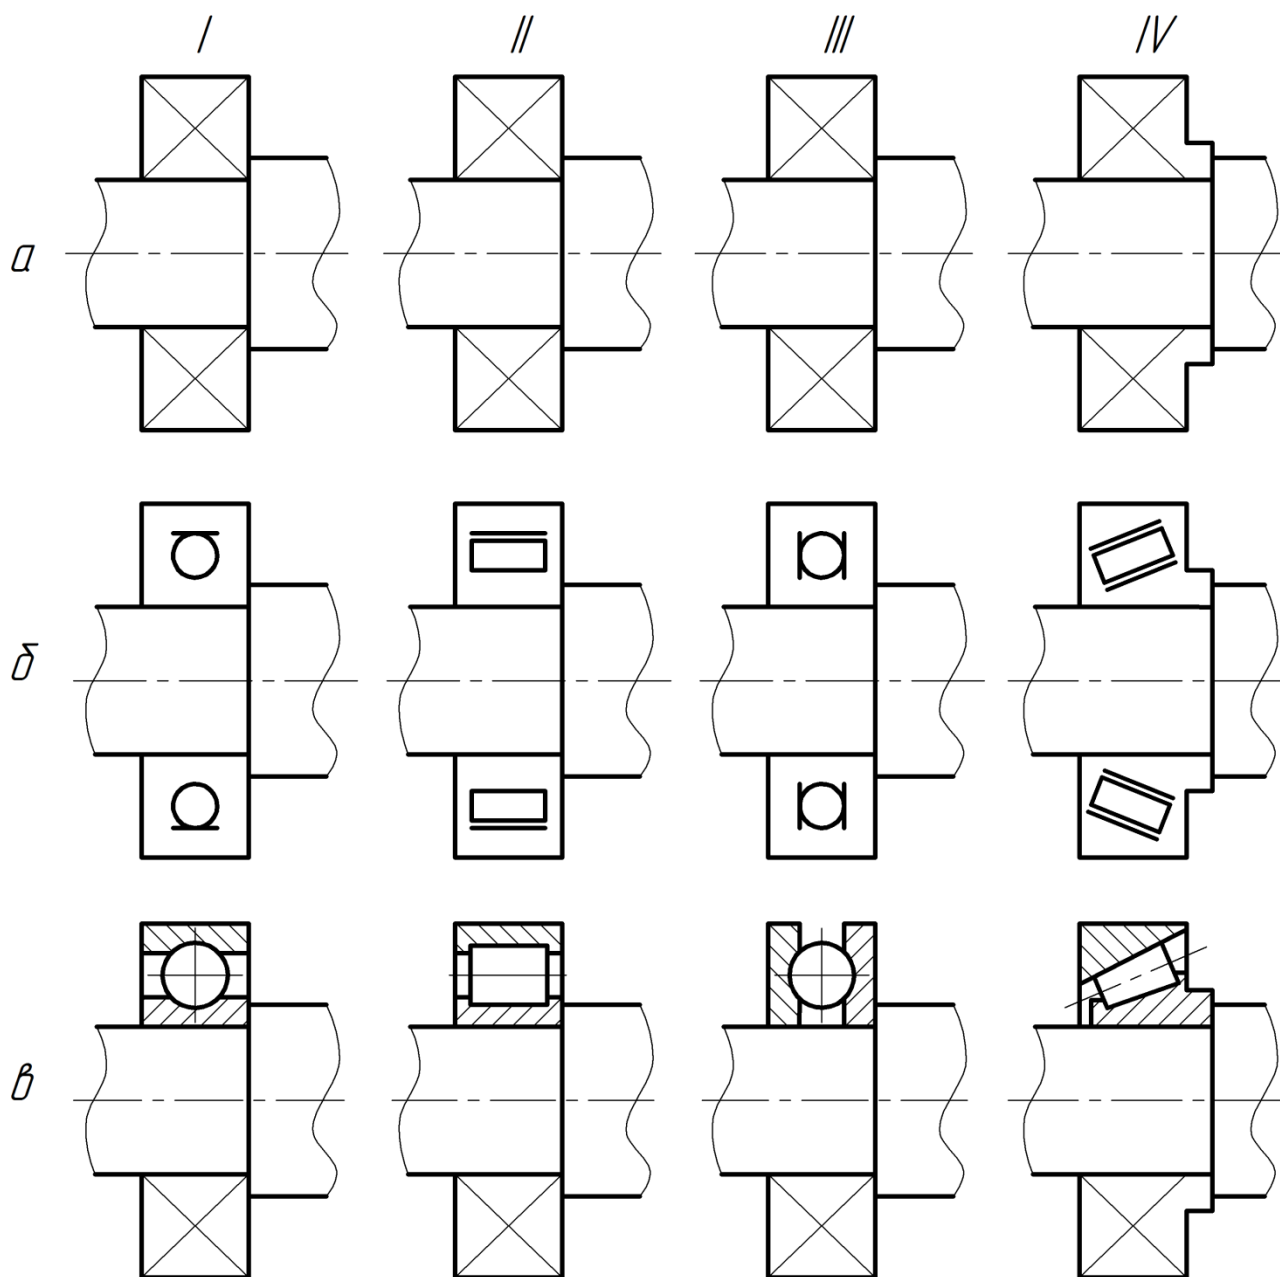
Изображение подшипников на сборочных чертежах:
